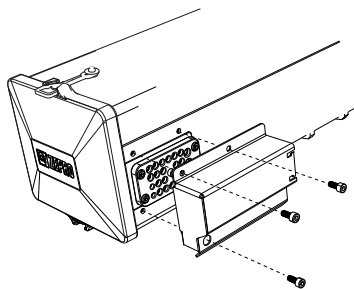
Die Schutzabdeckung der Kabeldurchführung ist mit drei Schrauben befestigt
